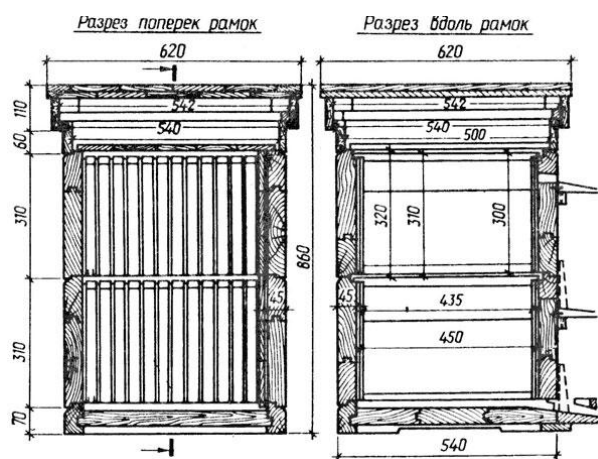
Чертеж двухкорпусного улья на 12 рамок (без магазинной надставки)
